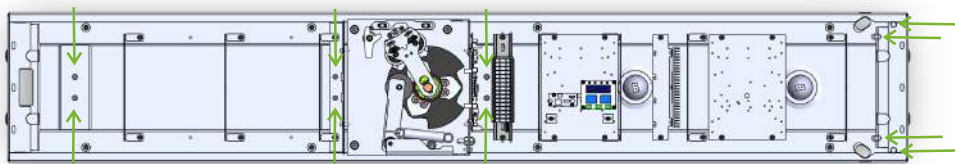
Отверстия для крепления корпуса механизма
